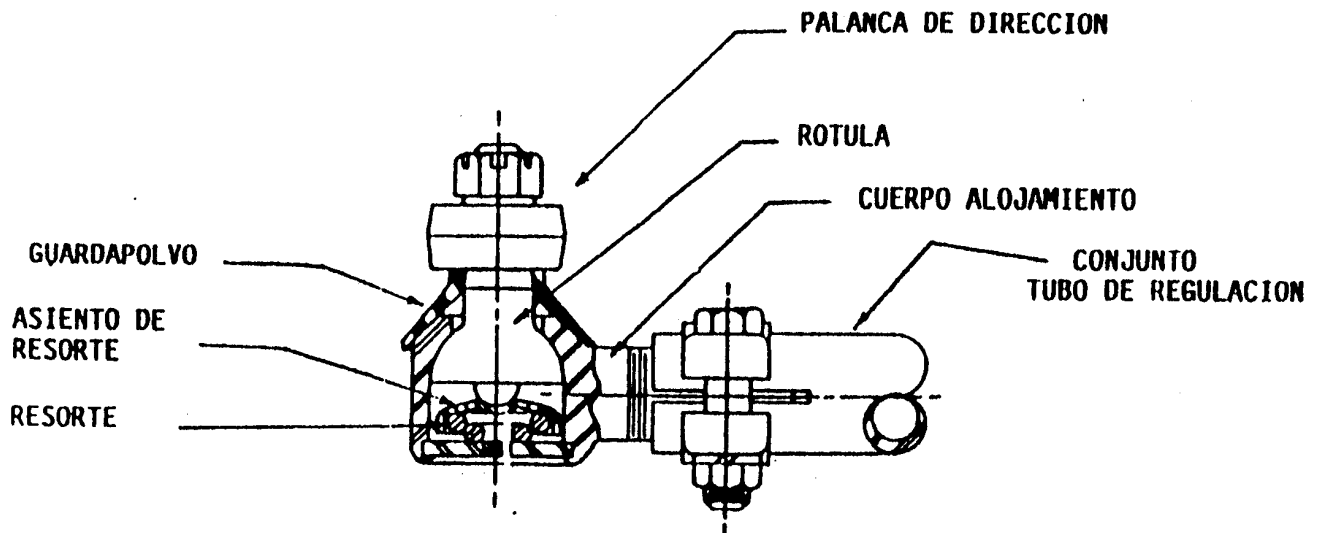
Terminal de rotula sin cojinete de fricción de contacto directo rótula-alojamiento.
